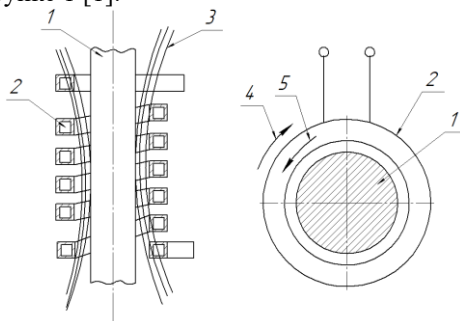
Схема индукционного нагрева: 1 – нагреваемая деталь; 2 – виток индуктора; 3 – магнитные силовые линии; 4 – направление тока в индукторе; 5 – направление тока в детали
